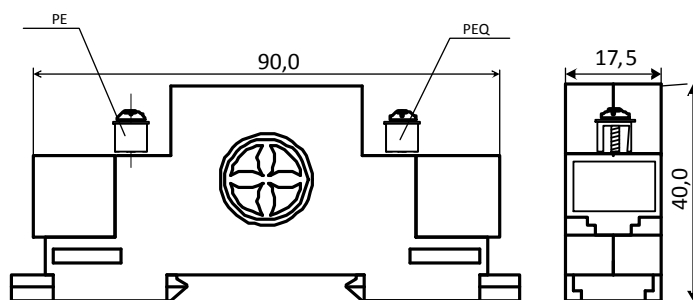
Габаритные размеры устройства Commeng Cat5P
